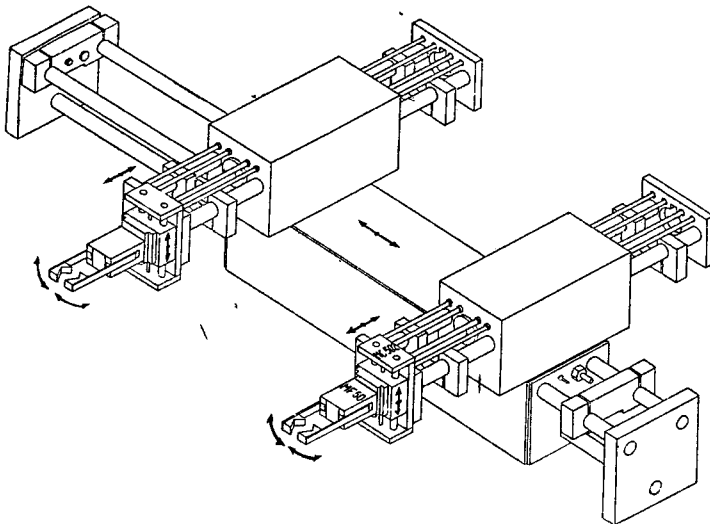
Zasada budowy konfiguracji części manipulacyjnej robotów PR-02 z modułów podstawowych
